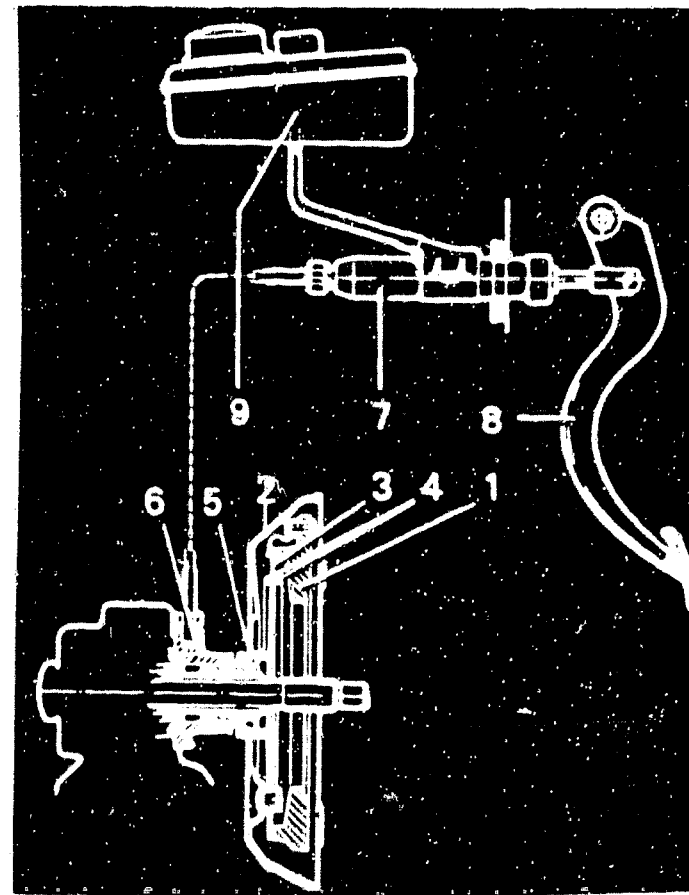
Kupplungsbetätigung: 1 Druckplatte – 2 Deckel – 3 Tellerfeder – 4 Kippringe – 5 Ausrücklager – 6 Ausrückzylinder – 7 Zylinder – 8 Kupplungspedal – 9 Reservoir.
